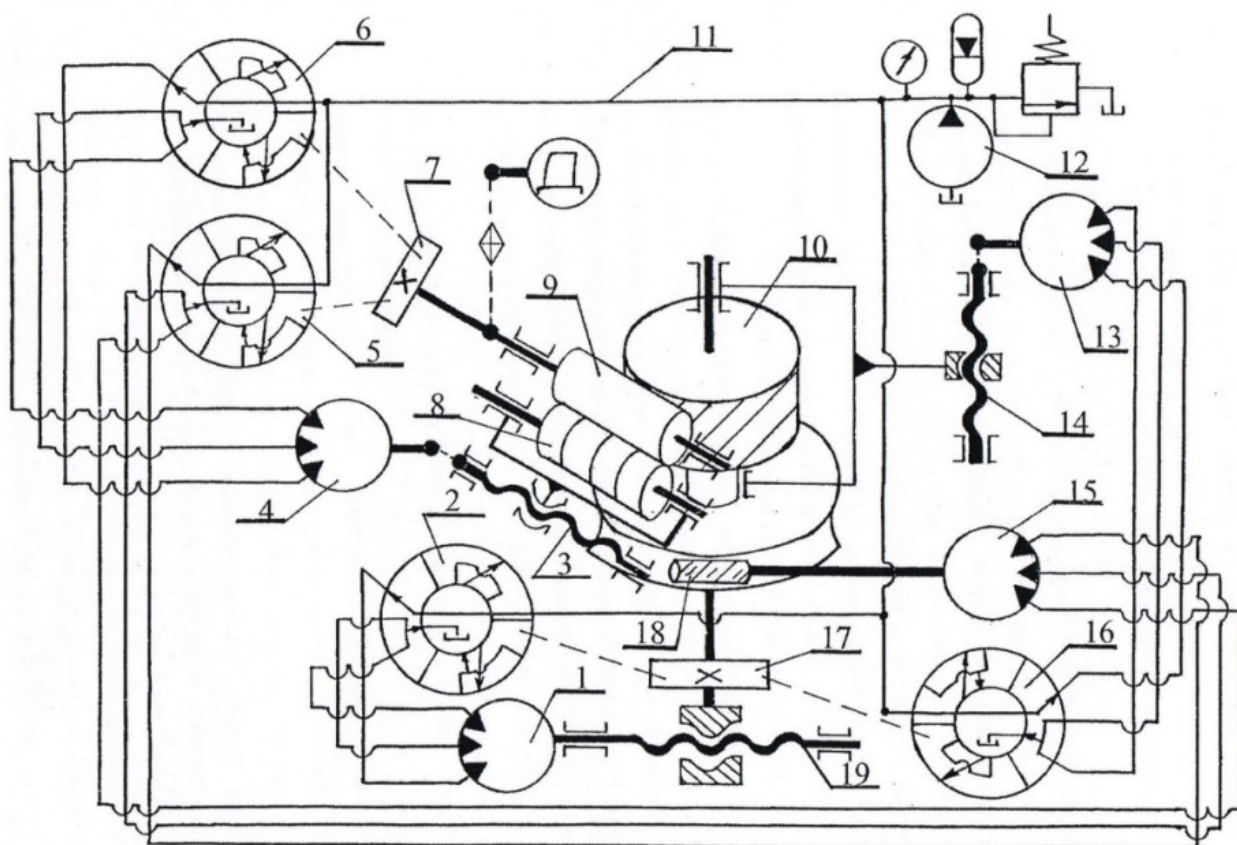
Структурная схема зубошлифовального станка с внутренними гидравлическими связями для шлифования зубьев цилиндрических зубчатых колес абразивным червяком
